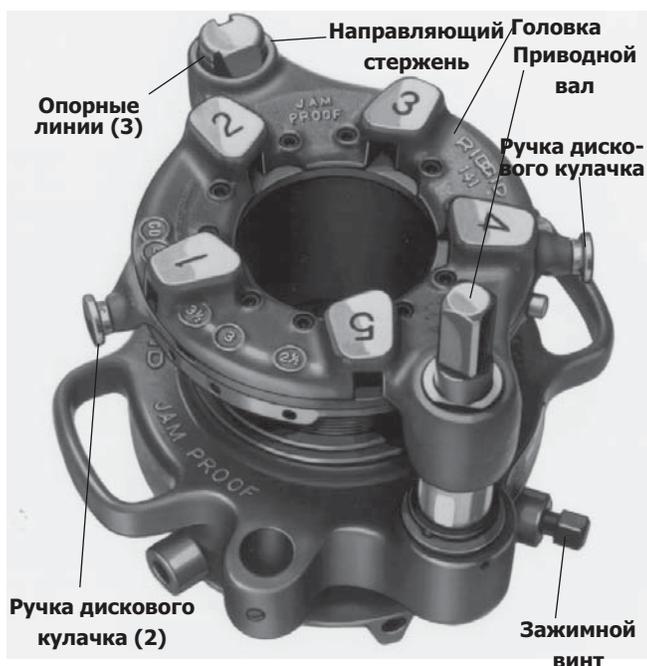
Головка №141 с зубчатой передачей с опорными линиями зубчатой втулки и направляющего стержня
